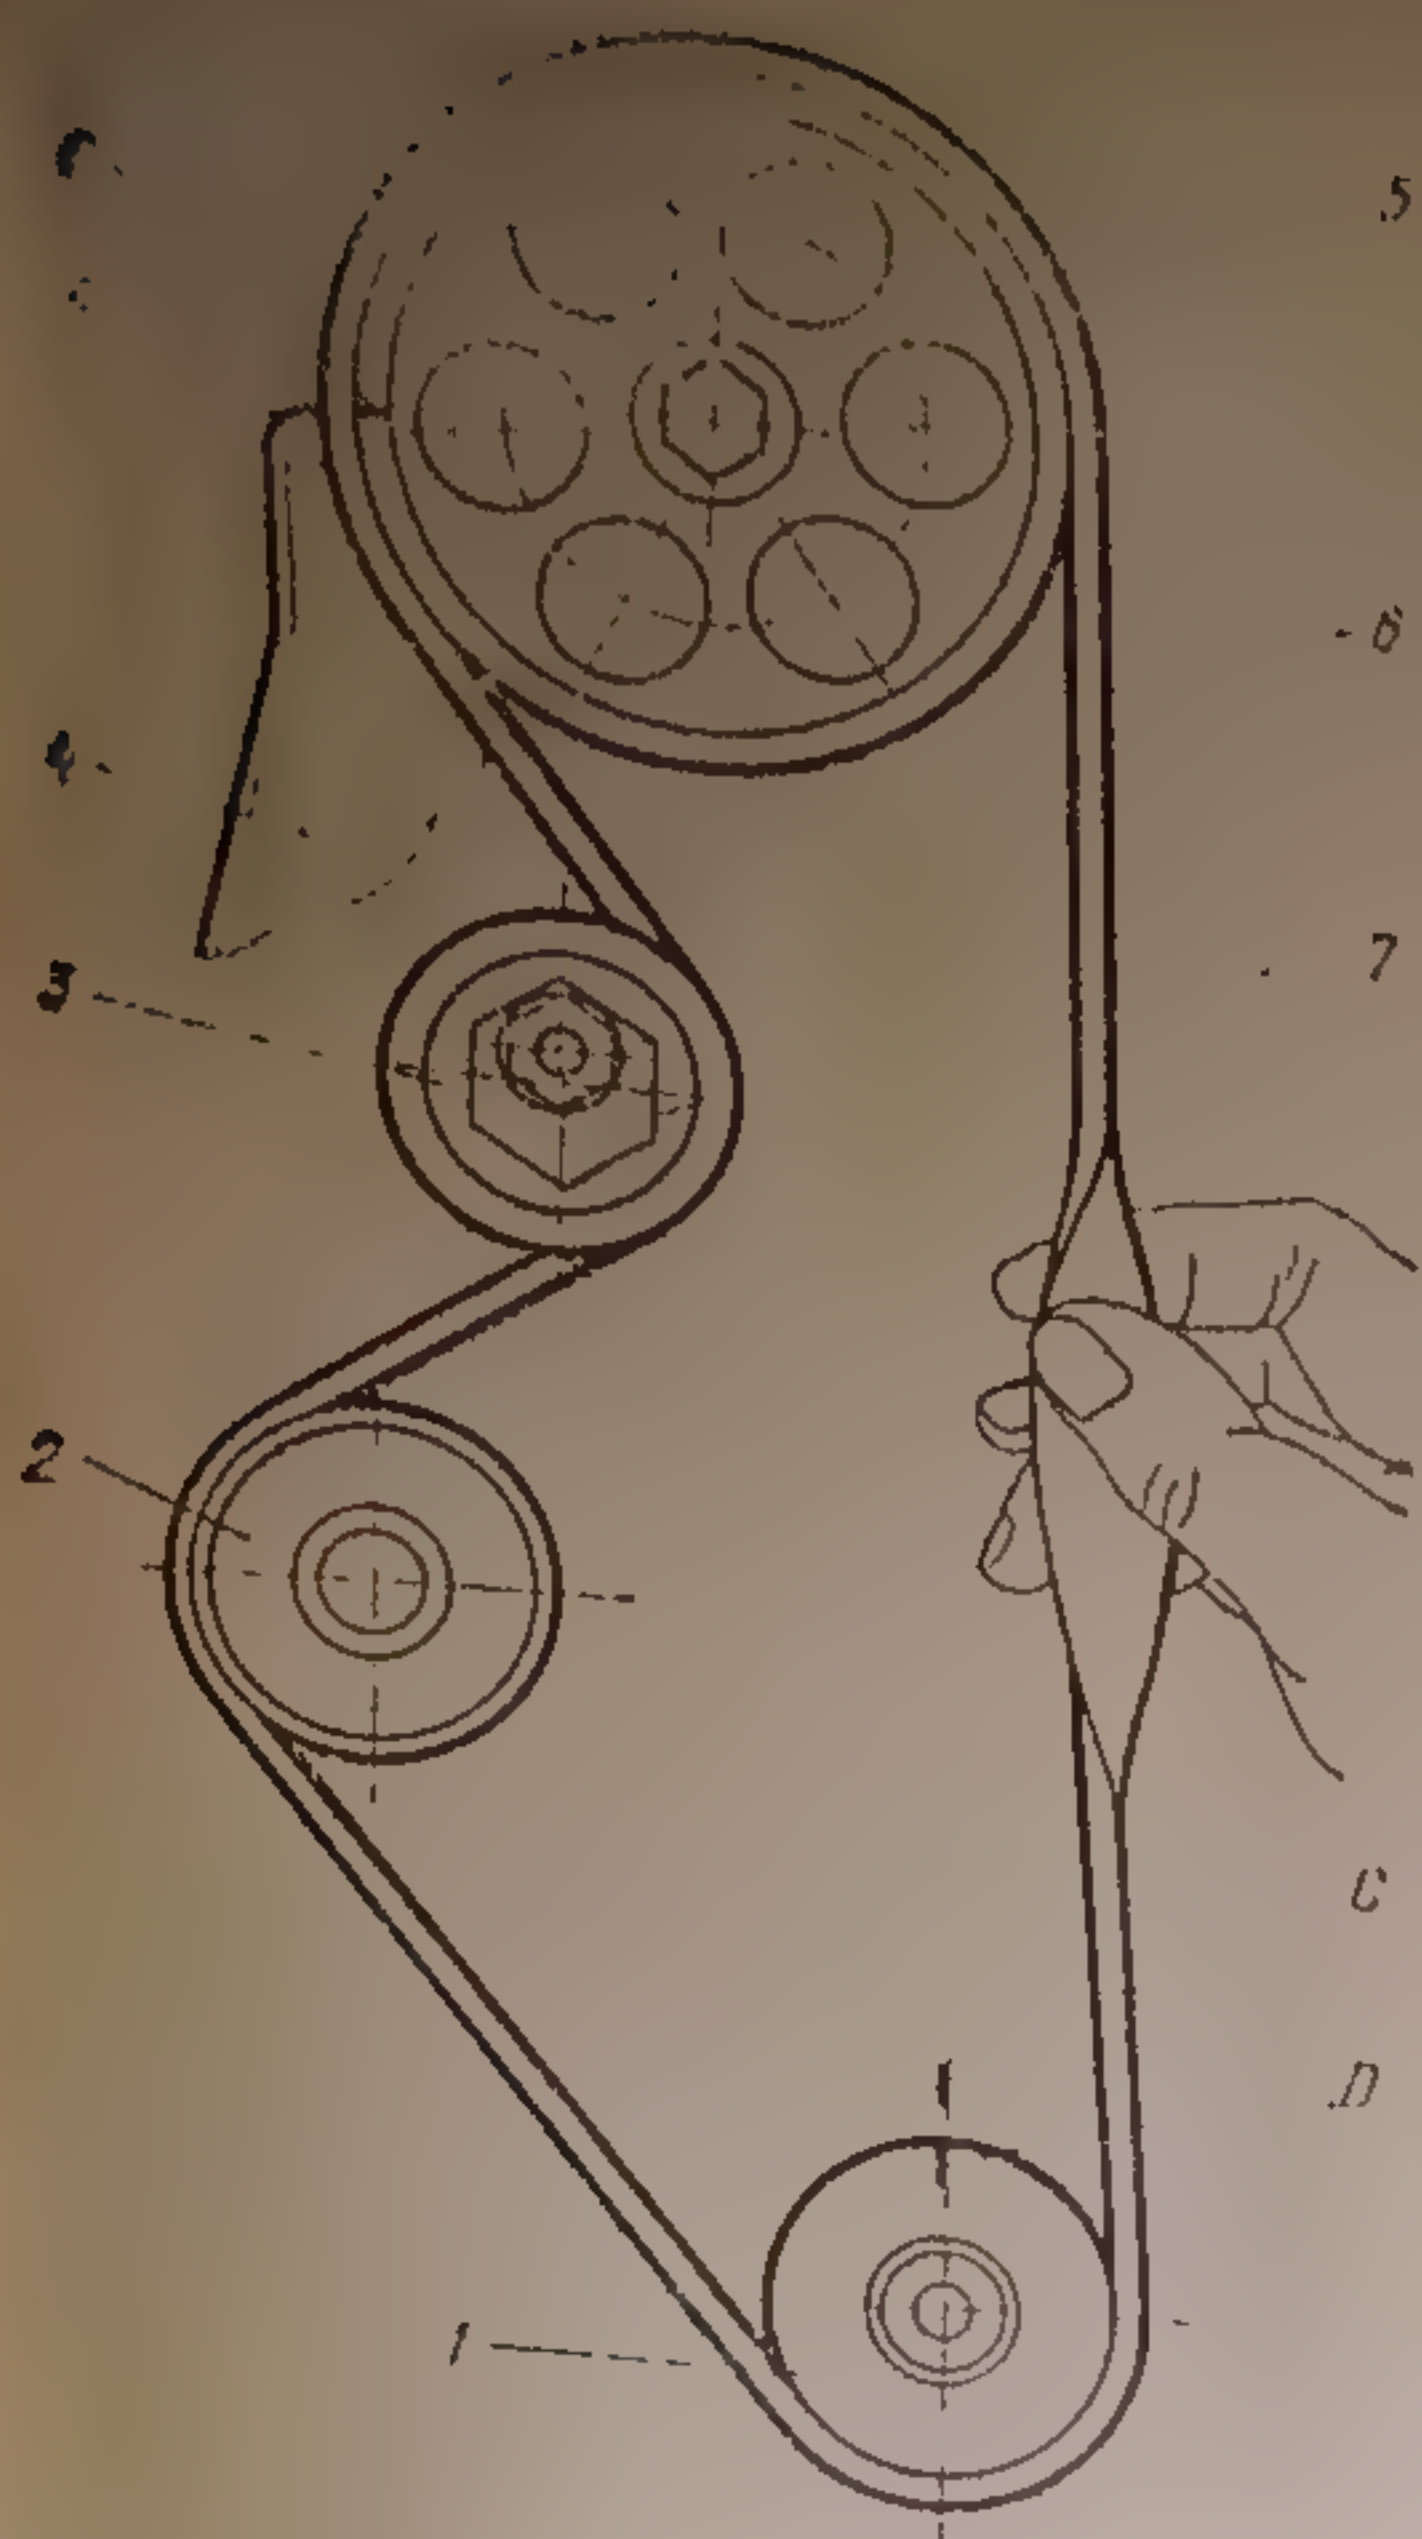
Привод распределительного вала двигателя ВАЗ-2108: 1 — зубчатый шкив коленчатого вала; 2 — шкив насоса охлаждающей жидкости; 3 — натяжной ролик; 4 — задняя крышка зубчатого ремня; 5 — шкив распределительного вала; 6 — зубчатый ремень; 7 — ось натяжного ролика; А — установочный усик на задней крышке зубчатого ремня распределителя; В — метка на шкиве распределительного вала; С — метка на крышке масляного насоса; D — метка на шкиве коленчатого вала.
